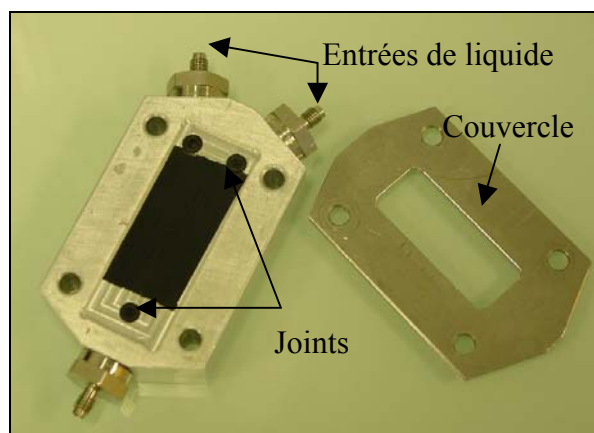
Boîtier usiné en aluminium constitué du socle et du couvercle.
